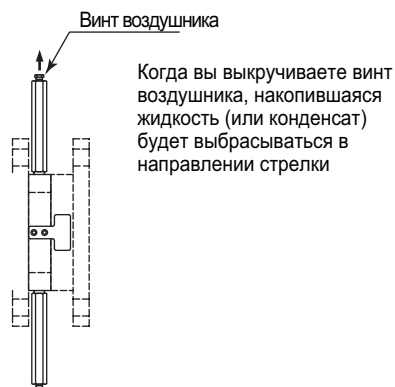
Удаление газа из промывочного соединительного кольца C10FR
